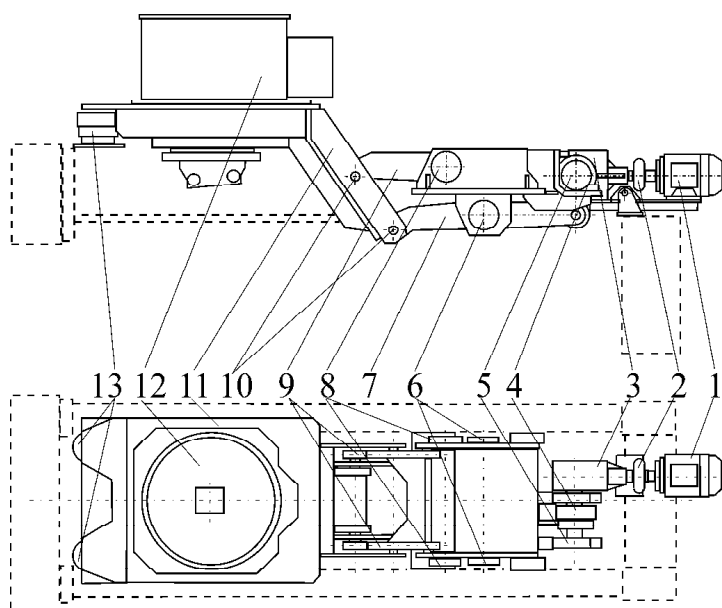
Загальний вигляд шарнірно-важільного коливного механізму кристалізатора МБЛЗ з електромеханічним приводом
